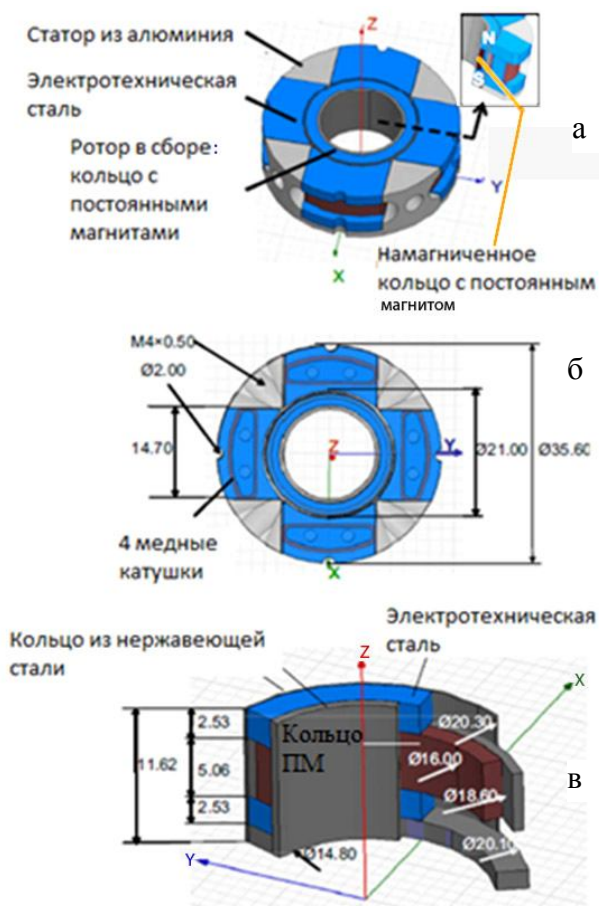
Структура гибридного магнитного подшипника [12]: общий вид (а), вид по Z (б), разрез (в)
